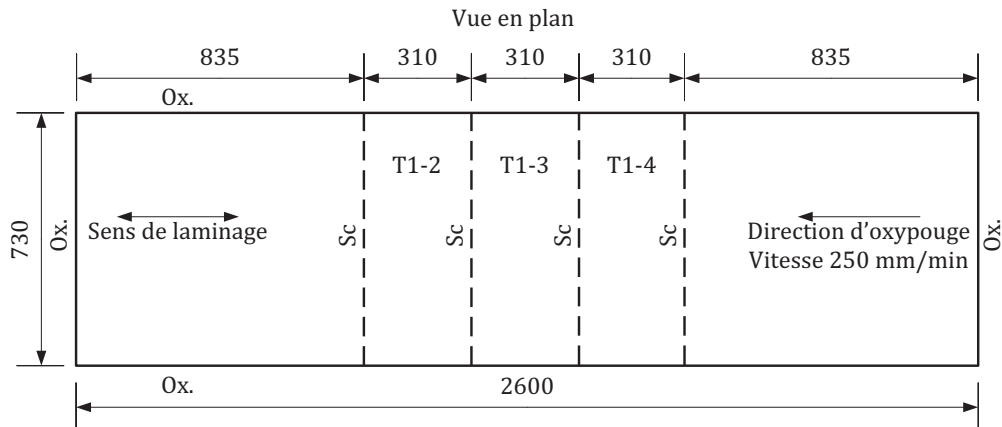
Emplacement des spécimens pour T1 (Ox : oxycoupé et Sc : scié) (en mm).
